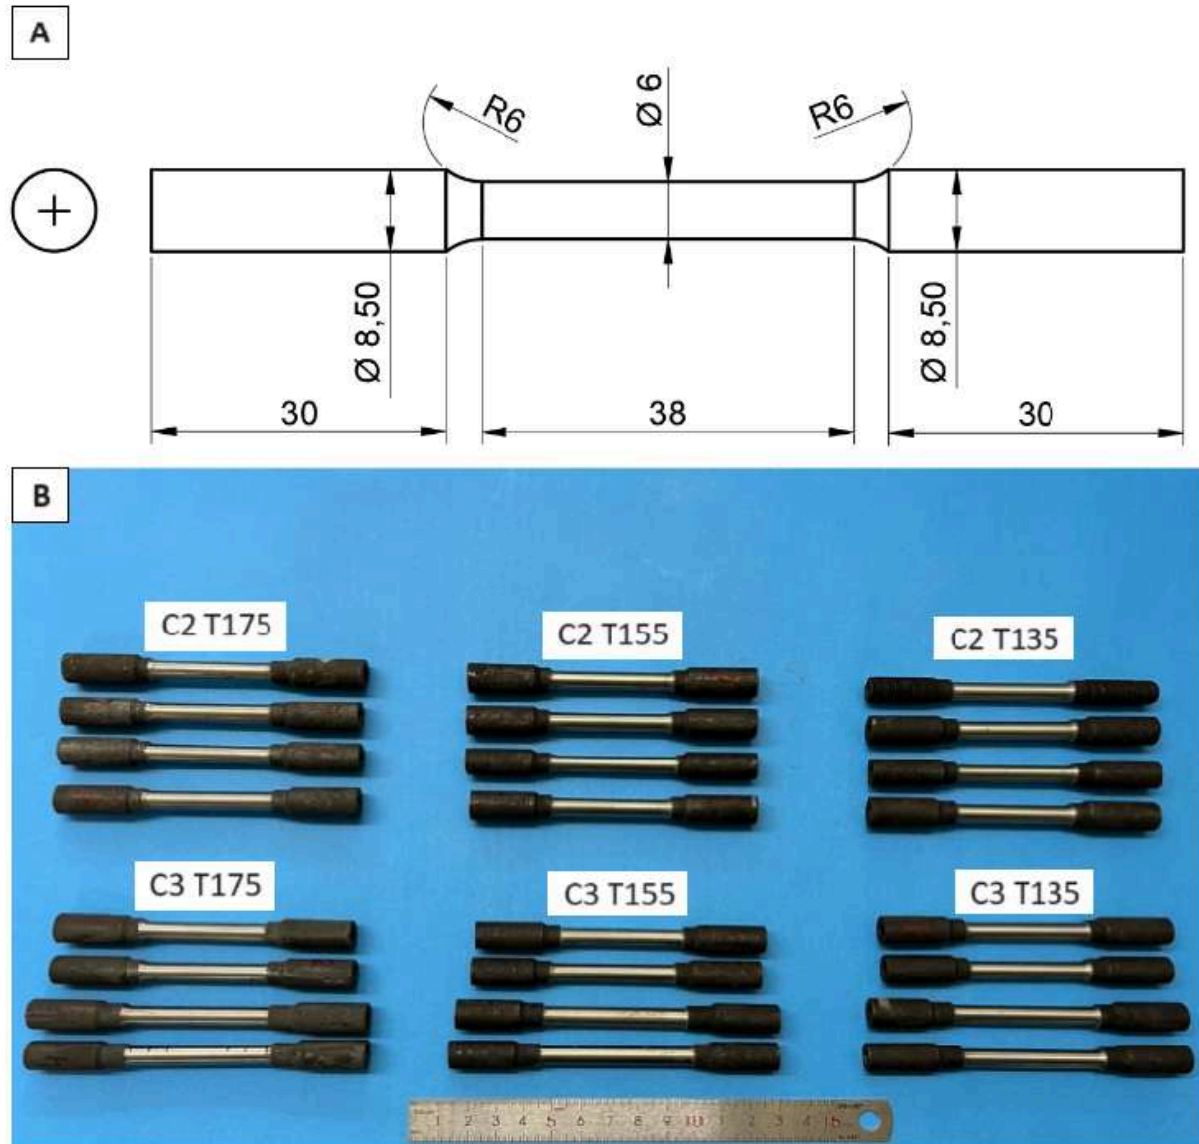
(A) Croquis de las probetas para ensayo de tracción.
